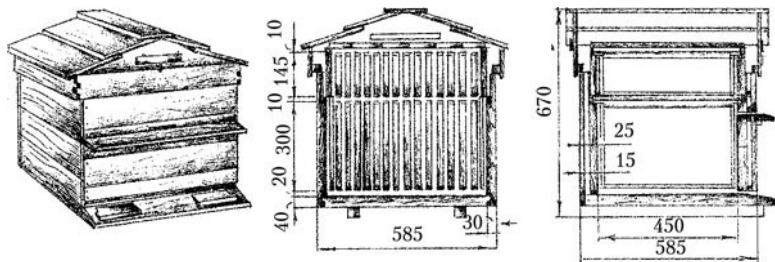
14-рамочный утепленный улей: а – общий вид; б – поперечный и продольный разрез
